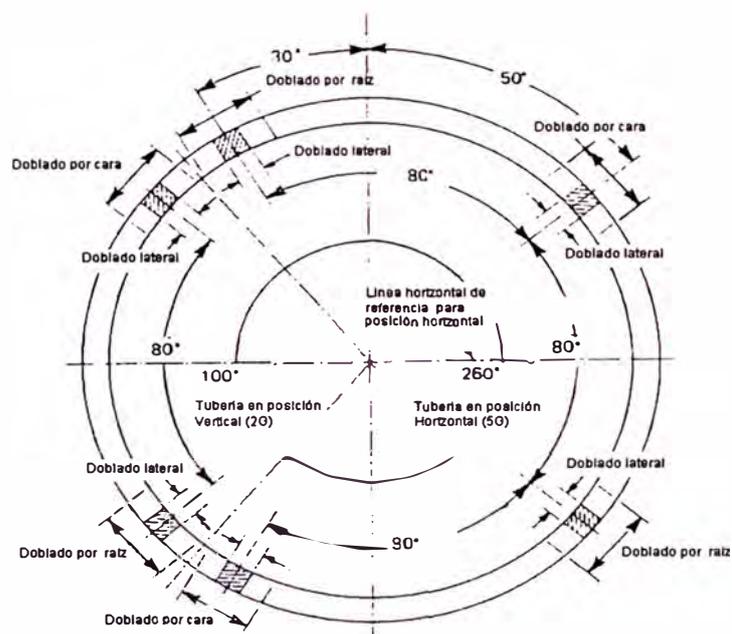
Posición de probetas para soldadura a tope de tuberías
